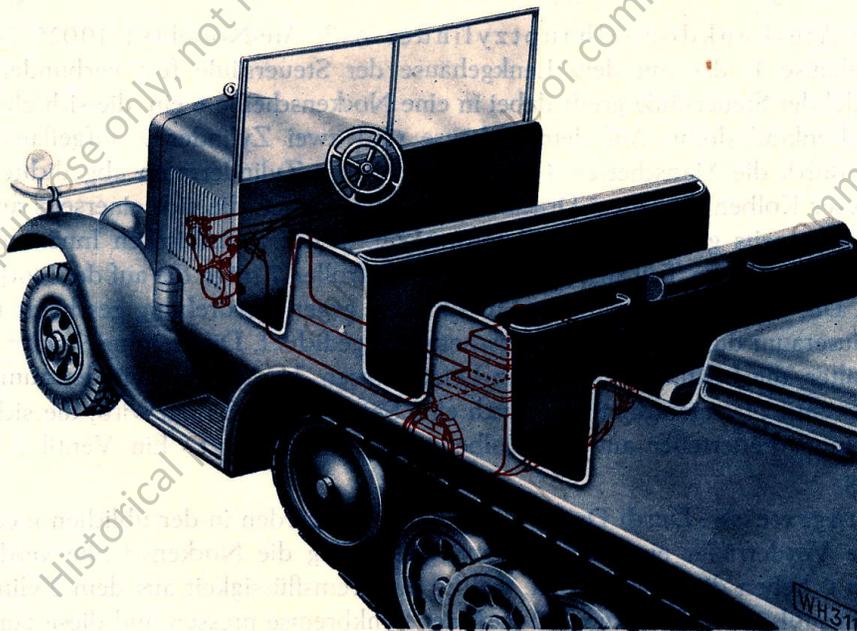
Olddruck-Lenkbremse im Halbkettenfahrzeug
